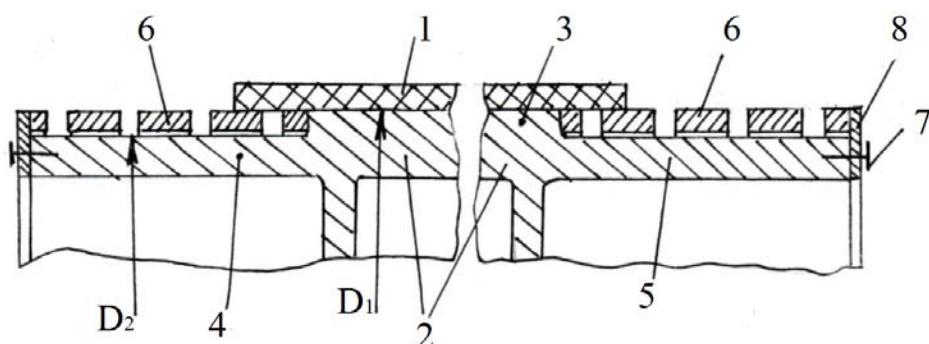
Приводной барабан ленточного конвейера [5]
